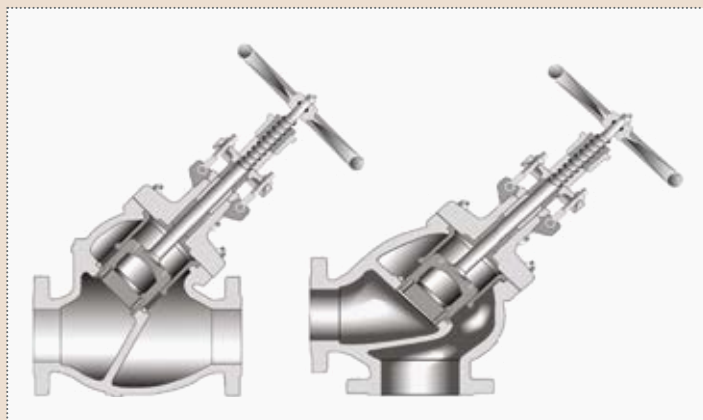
Два варианта корпусов клапанов с выдвижным штоком (внешней резьбой)
